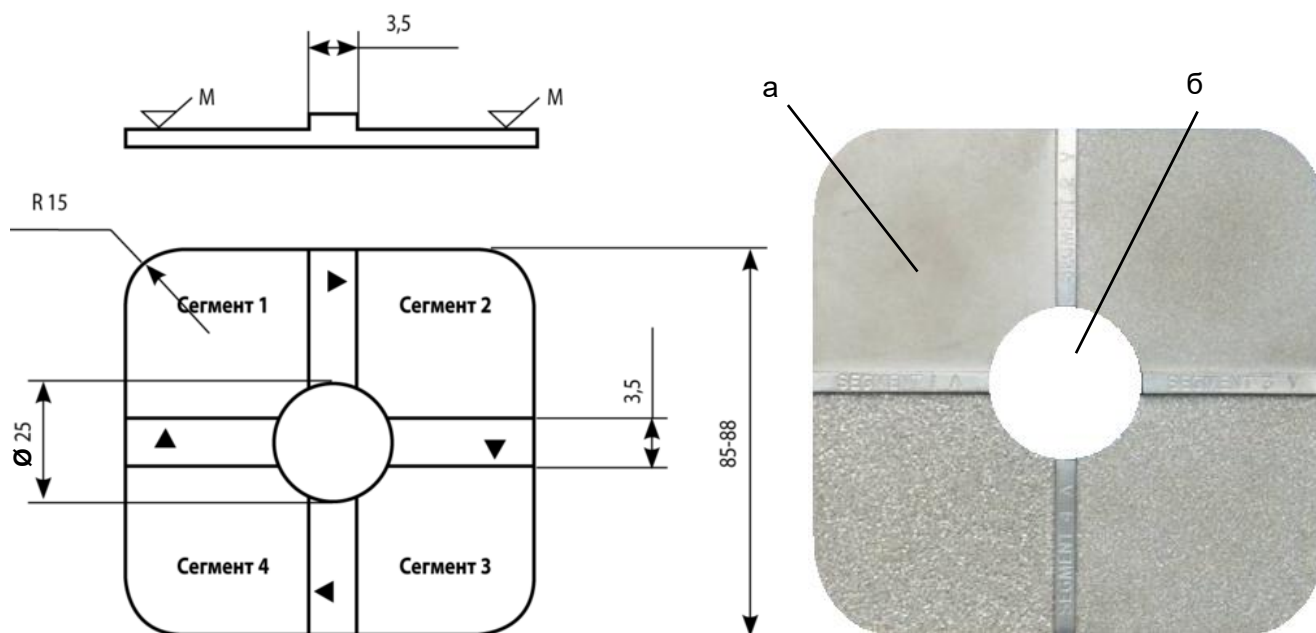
ISO-компаратор профиля шероховатости поверхности:
